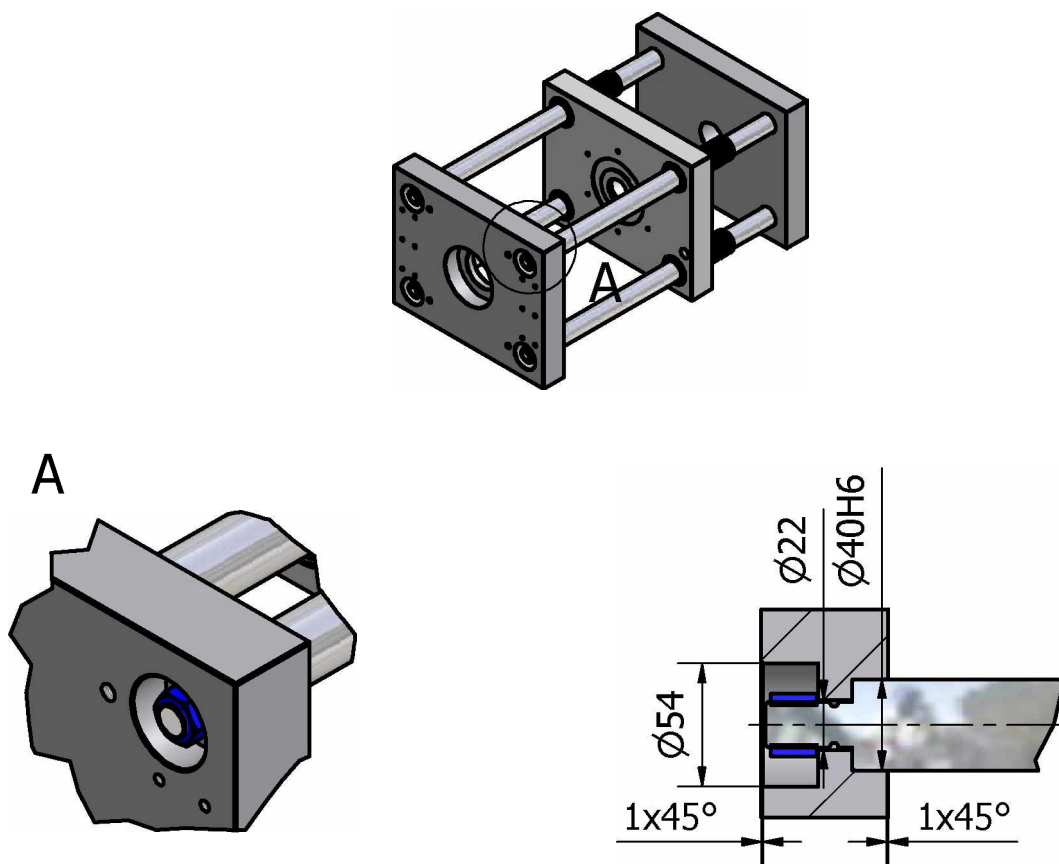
Befestigung der Säulen an den Grundplatten: Die vier Säulen wurden mit beidseitigem Rechtsgewinde gefertigt und mit Muttern in die Platten verschraubt.
